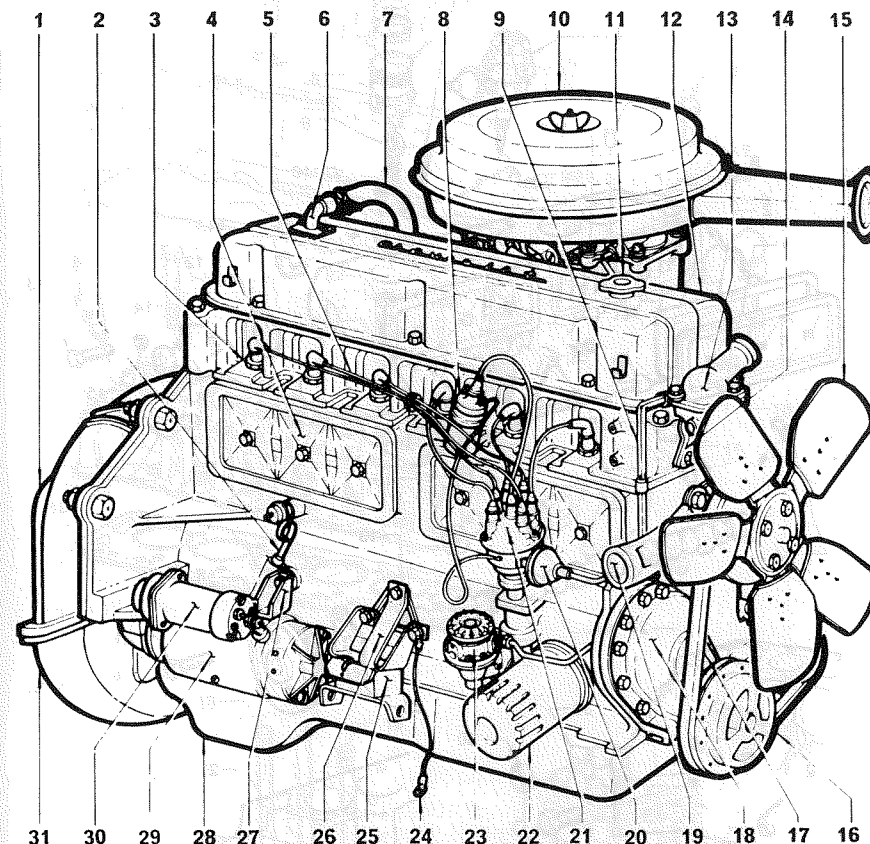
Motor de seis cilindros (vista do lado direito).
